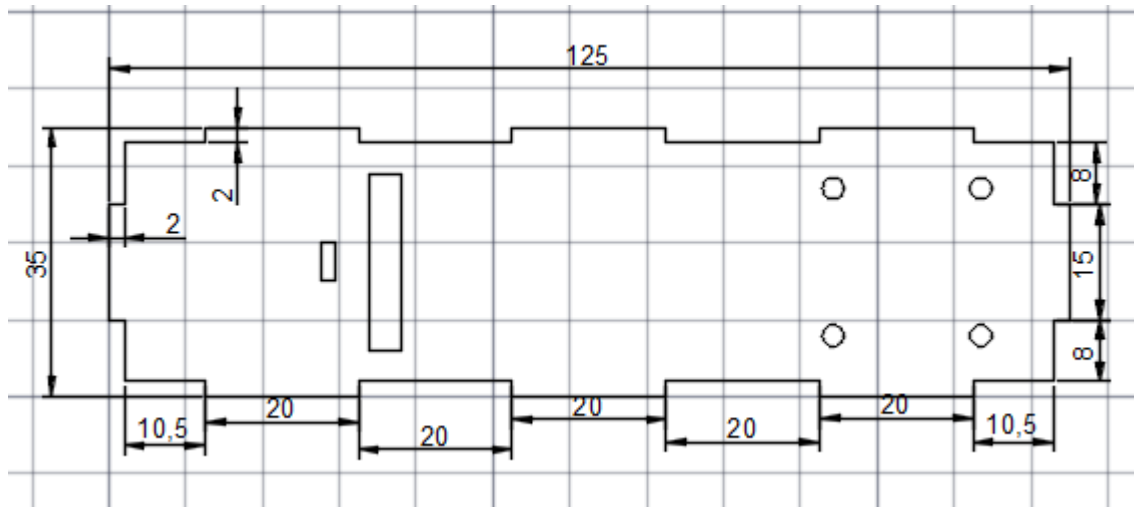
pieza lateral derecha e izquierda, cotas externas.
